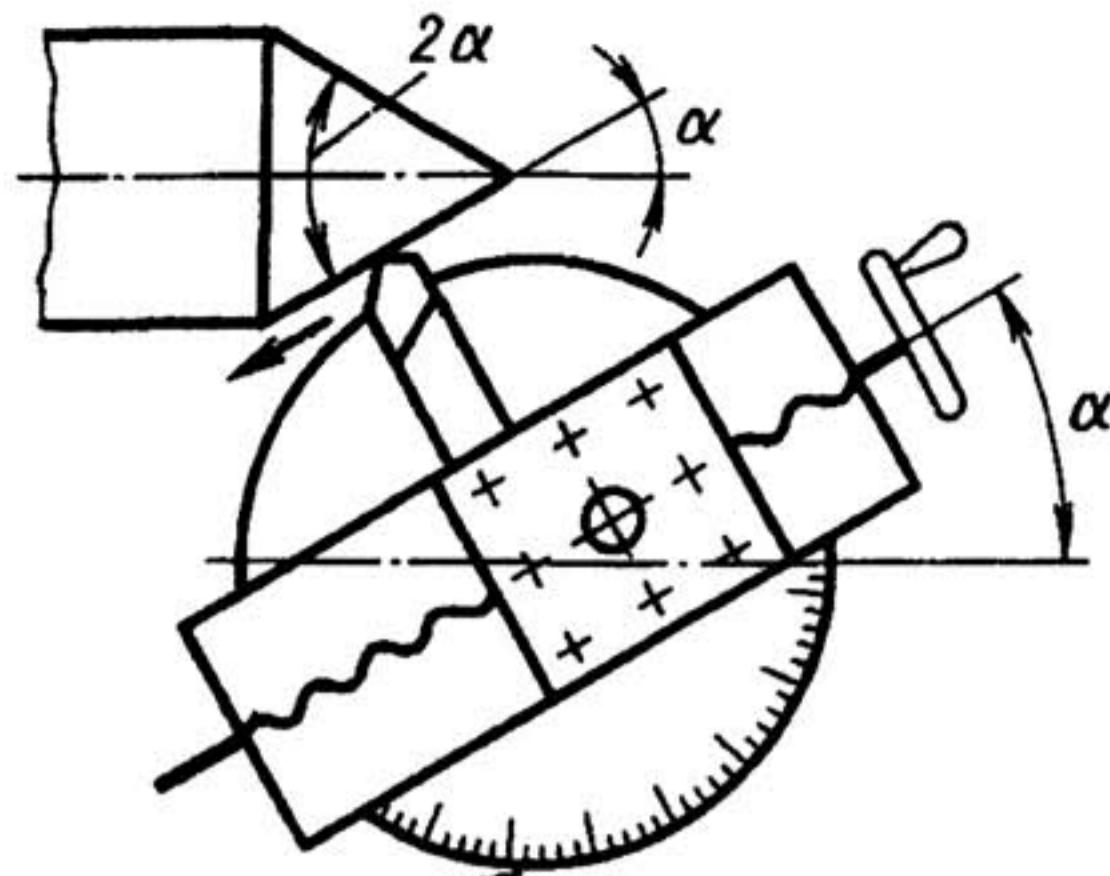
Обработка конуса при повороте верхних салазок суппорта с резцедержателем
